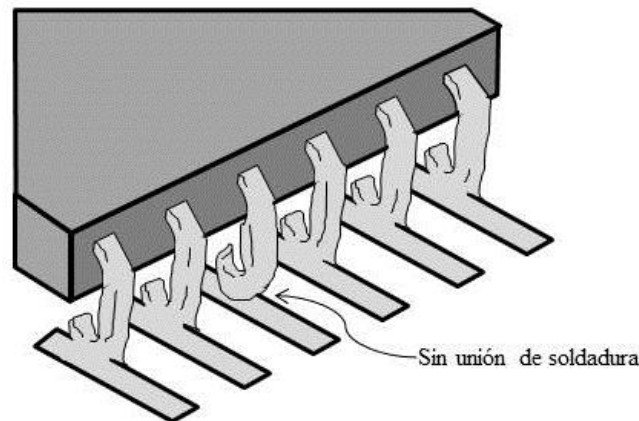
Ejemplo de capilaridad de soldadura en terminales J [2].
